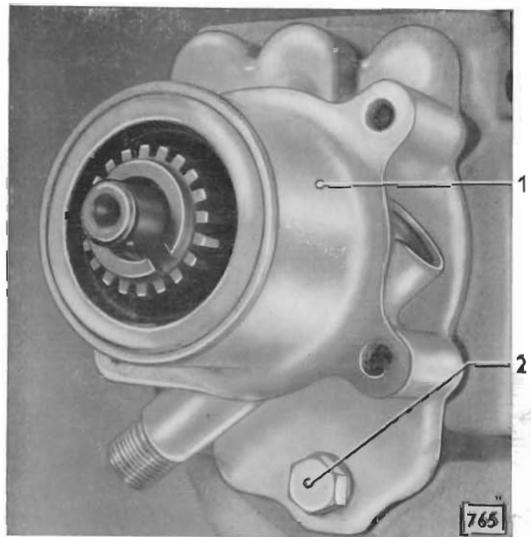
Getriebegehäuseendstück an Getriebegehäuse angeschraubt
